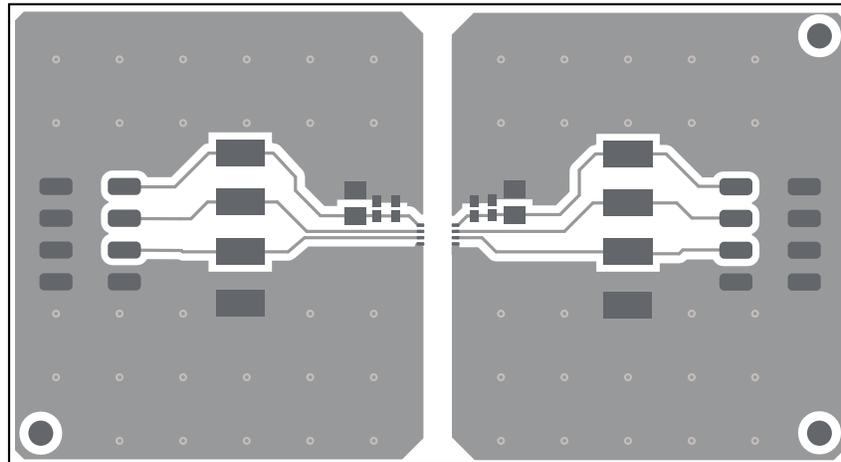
ISO6521REUEVM PCB 布局 - 顶层
